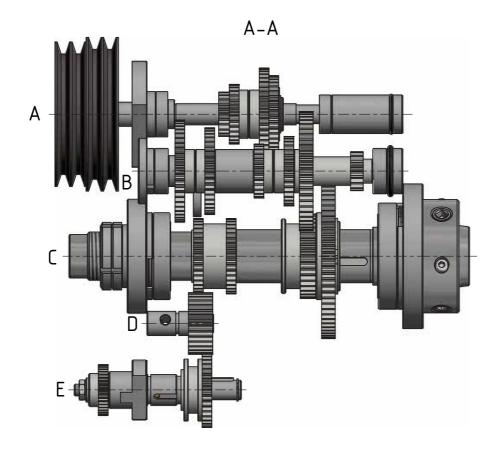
Getriebe Spindelstock 2-6 - Headstock gear 2-6
